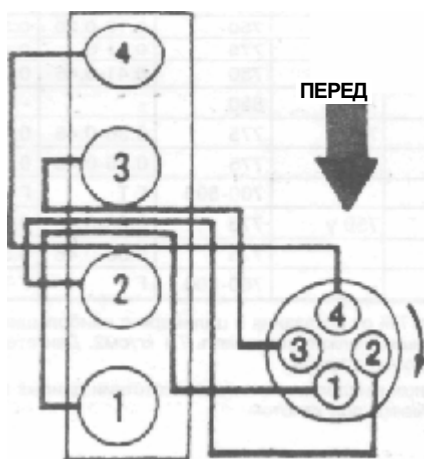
4-цилиндровые двигатели B230F, B230FT, 8234F. Порядок работы цилиндров: 1-3-4-2. Направление вращения распределителя: по часовой стрелке.
